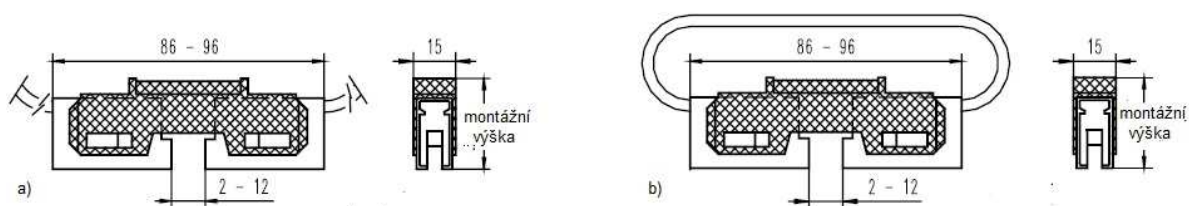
Spoje vodičů Wampfler a) šroubový b) zásuvný [18]
